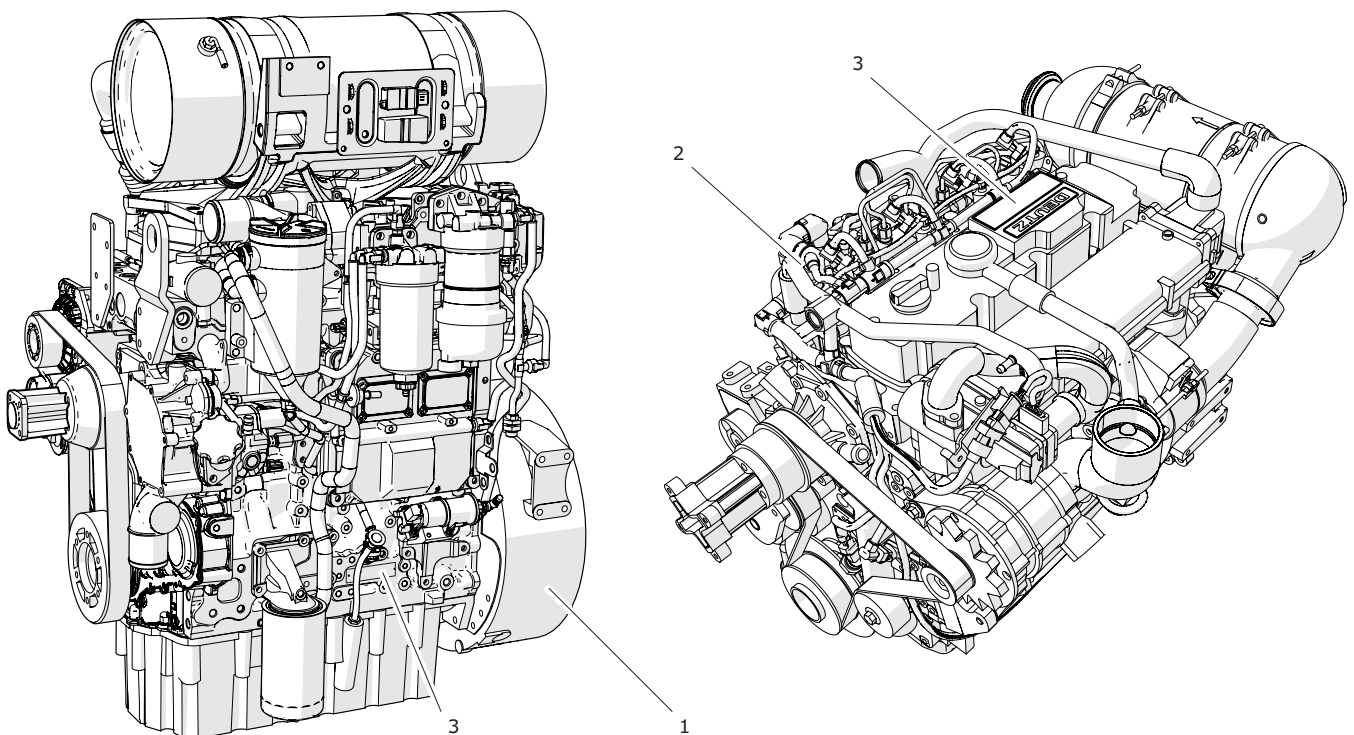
Emplacement de plaque signalétique du moteur à combustion
